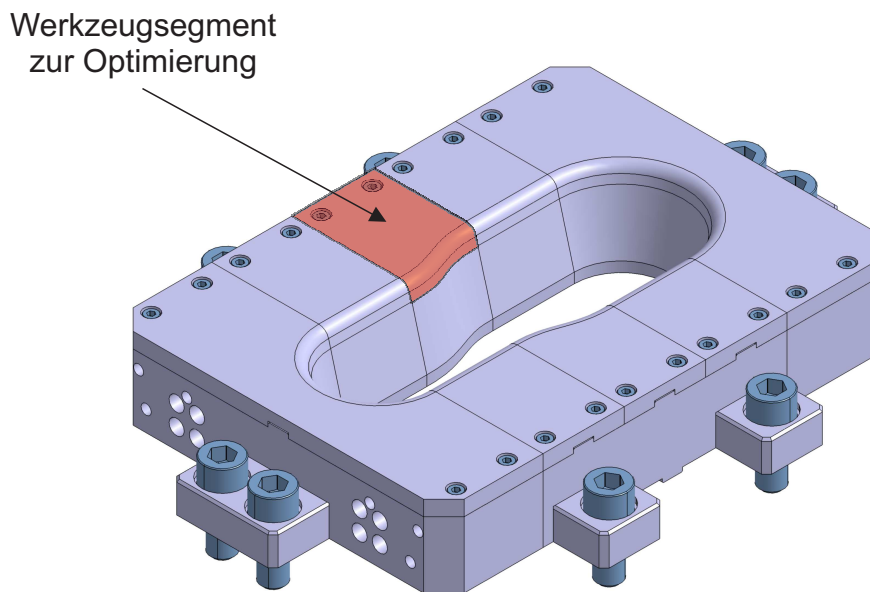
Prinzipskizze der zu beschichtenden Umformwerkzeugmatrize
